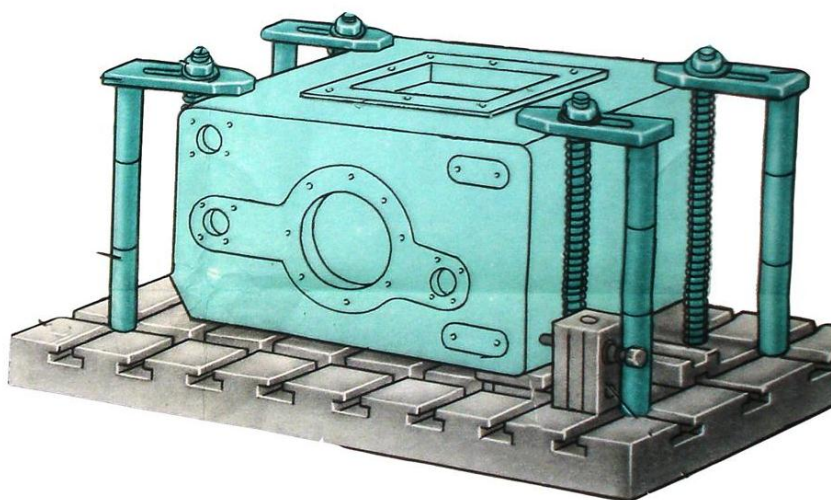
Крепление крупных заготовок для обработки нескольких отверстий
